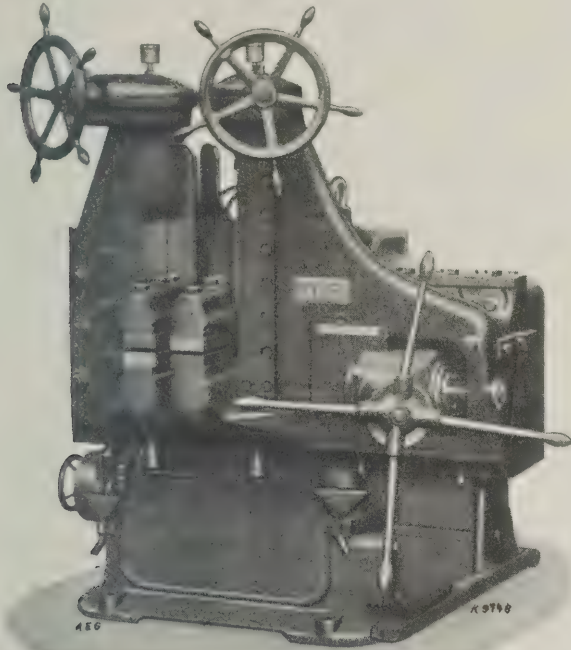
Stumpfschweißmaschine SR 80/105 für Handeinspannung.
